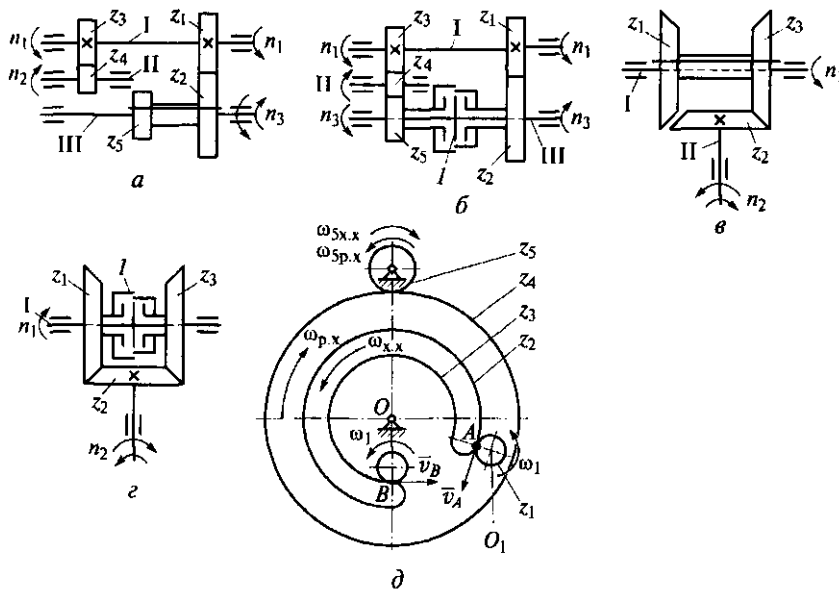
Механизмы реверса, составленные из цилиндрических (*а, б*), конических (*в, г*) зубчатых колес и в виде составного зубчатого колеса (*д*):
